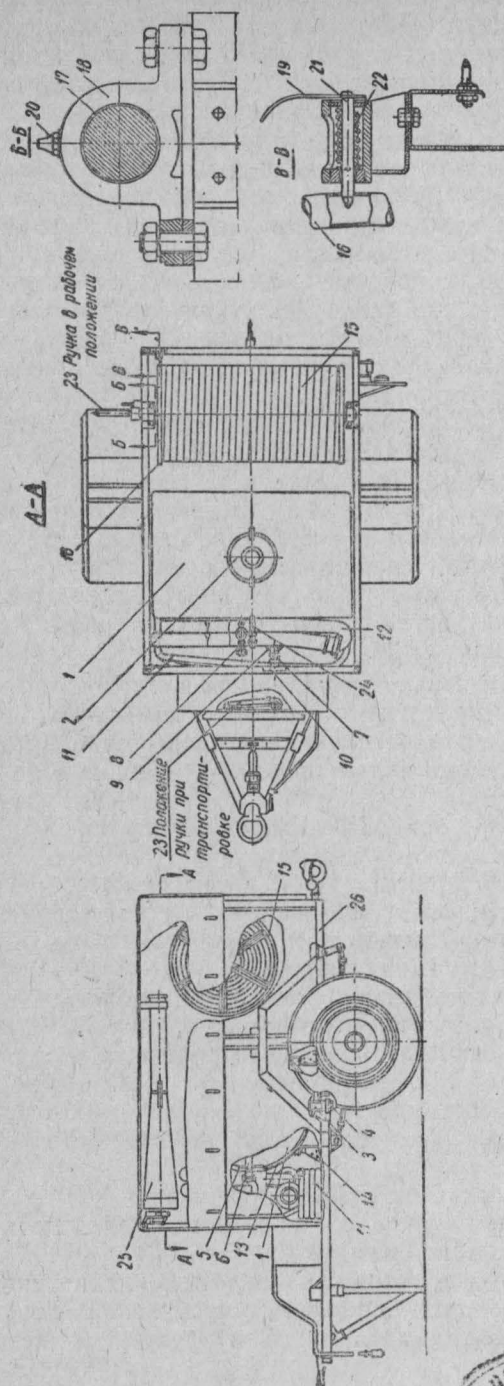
Цистерно-рукавный принцип ЦРП-20.
